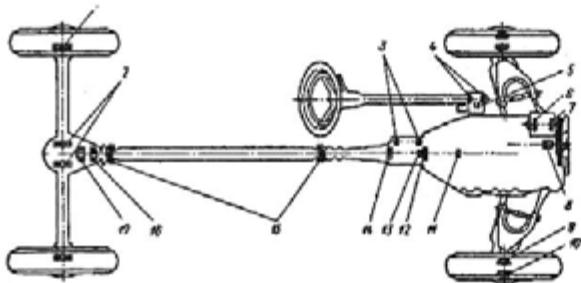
Схема расположения подшипников качения в агрегатах шасси автомобилей «Москвич-1500»
